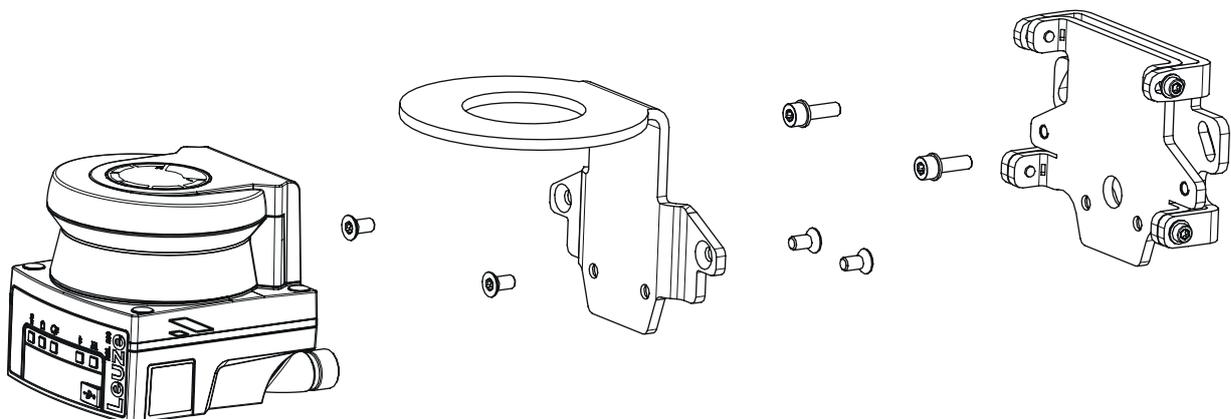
Montage mit Wandhalter und Schutzbügel
